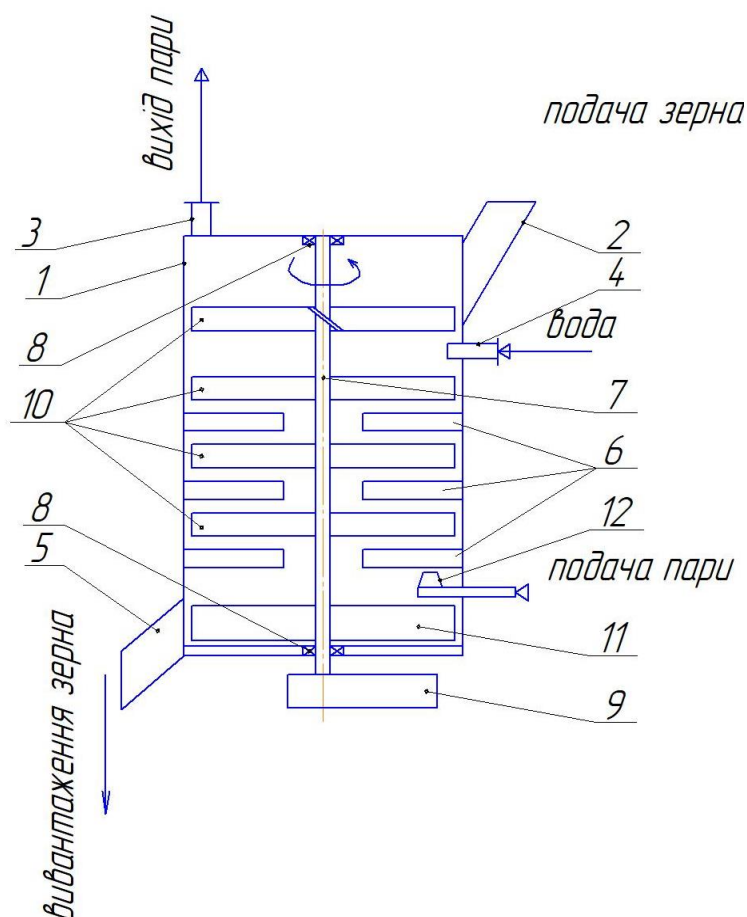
Принципова схема пропарювача для гідротермічної обробки зерна
